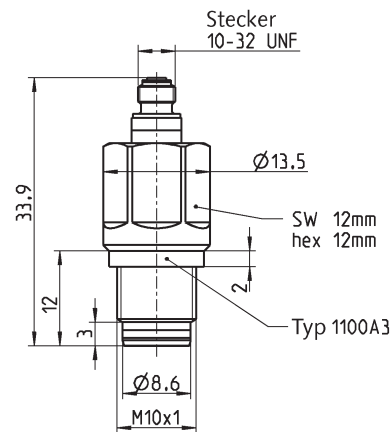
Zylinderdrucksensor Typ 6013C mit 10-32UNF Stecker
